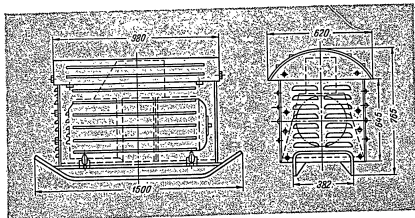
Габаритные размеры преобразователя частоты типа ПЧ-5
